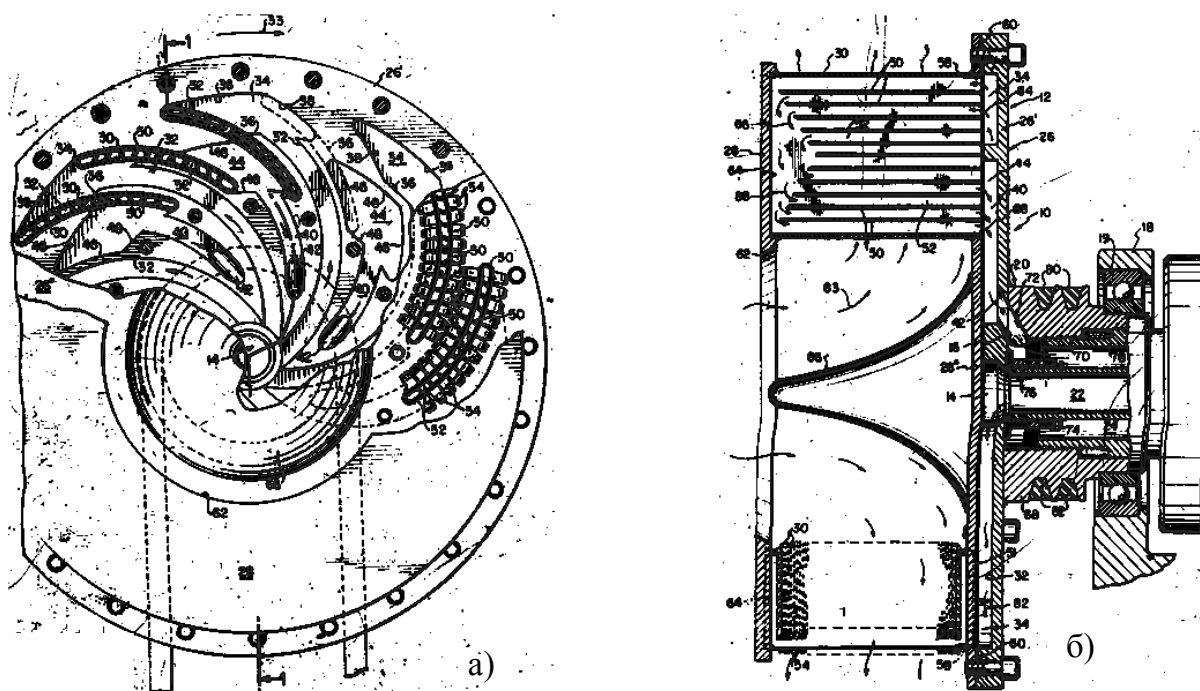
Роторный теплообменник: а) – вид спереди; б) – вид сбоку
